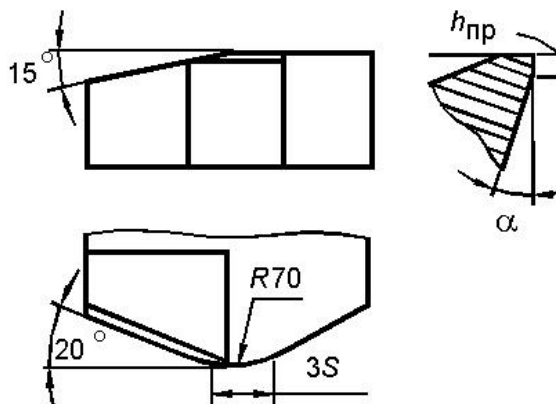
Форма режущего лезвия с криволинейной переходо-зачищающей кромкой, различными углами наклона зачищающей и главной кромок и предварительным притуплением задней поверхности
